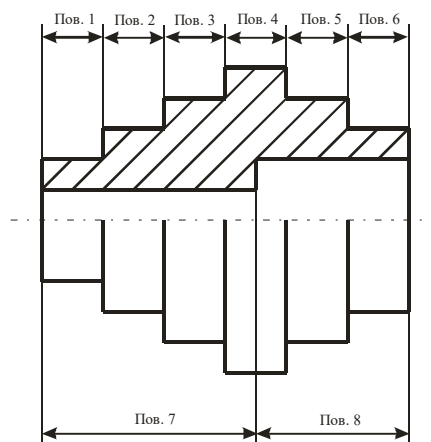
Комплексный эскиз обрабатываемой заготовки
